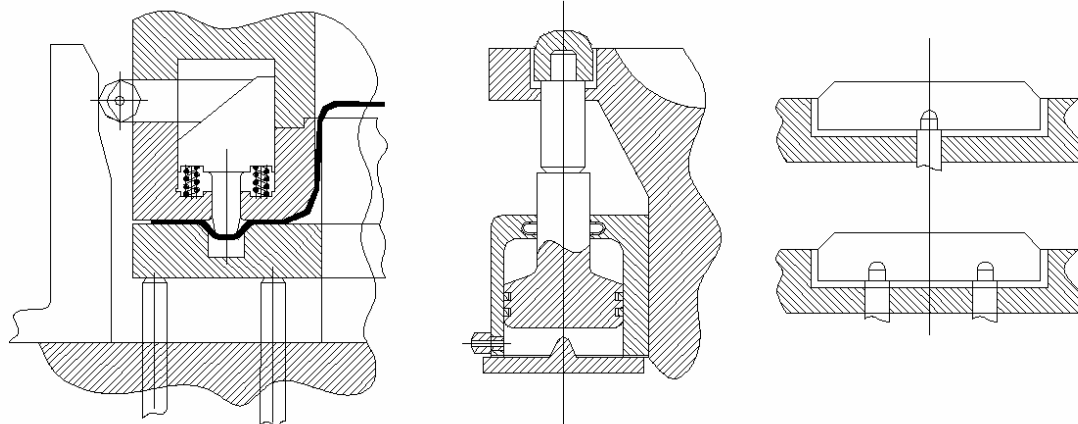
Способы увеличения усилия прижима к концу рабочего хода: а – при помощи клинового устройства; б – при помощи пневматических цилиндров; в – крепление опорных стержней
